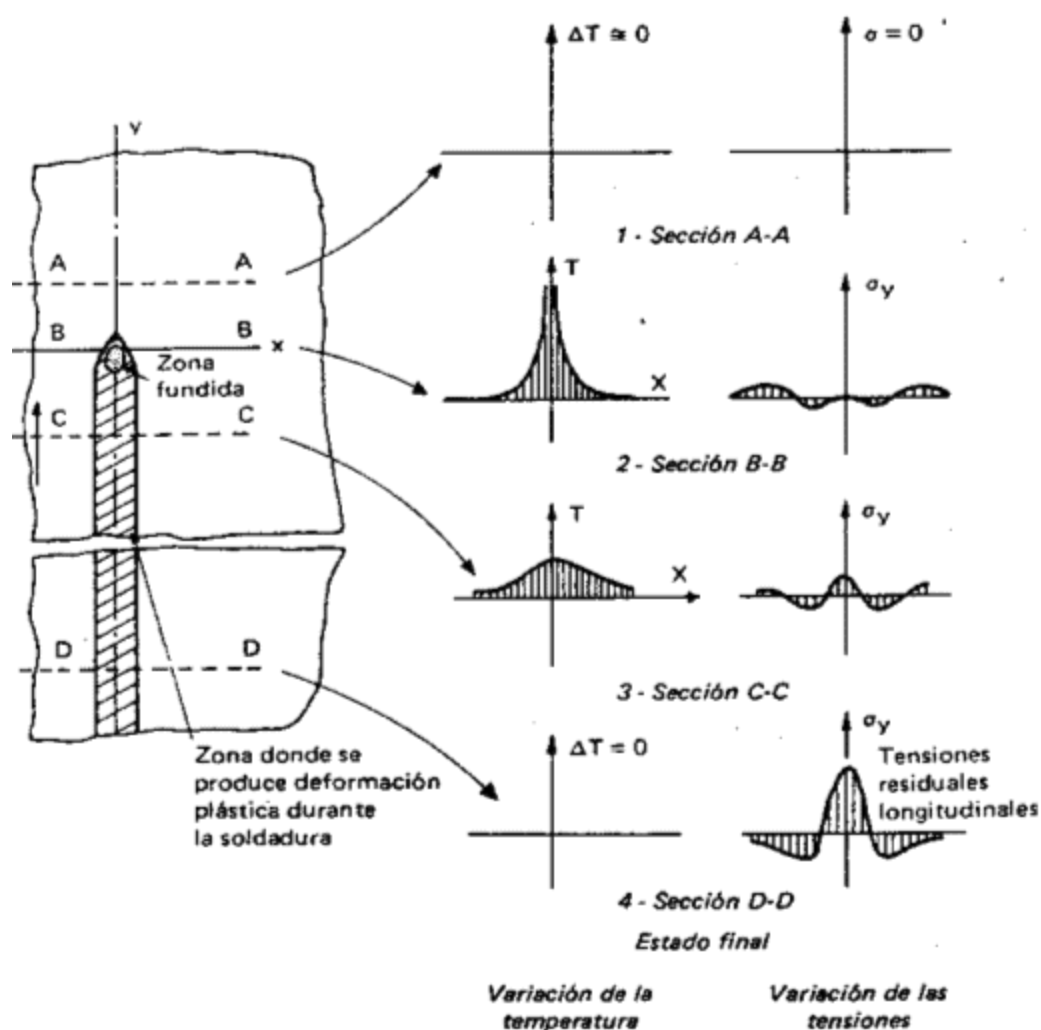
Esfuerzos de tensión y compresión durante la soldadura (Masubuchi, 1998).
